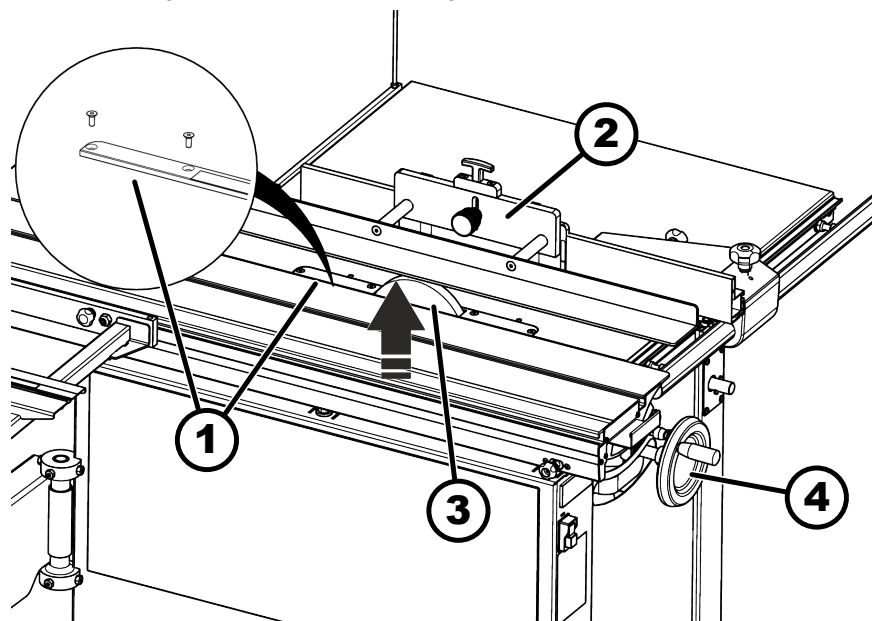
Placa de inserción para montar la herramienta de ranurado
